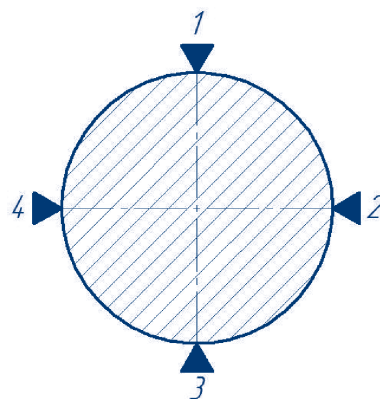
Схема измерения шероховатости обработанной поверхности детали
